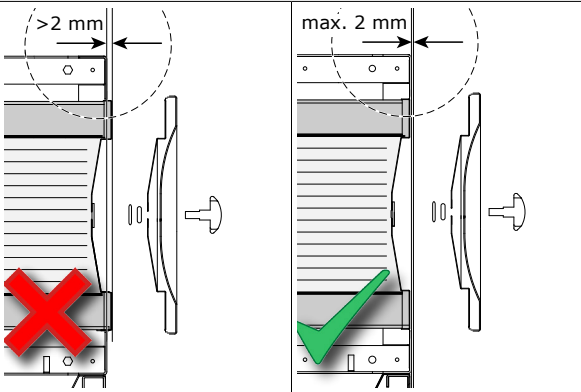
Couvercle d'inspection (1 ou 2)
